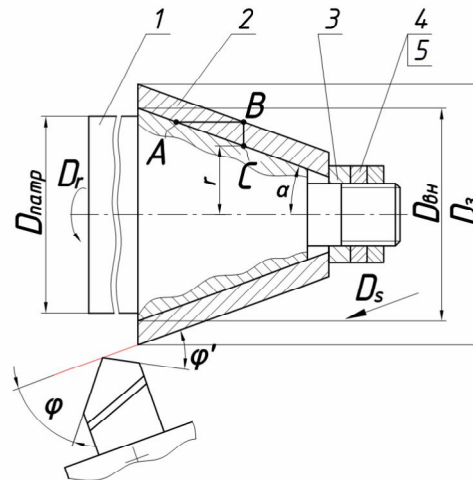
Схема обточування зовнішньої циліндричної поверхні зразка: 1 – правка; 2 – дослідний зразок; 3 – шайба; 4, 5 – гайка і контргайка
